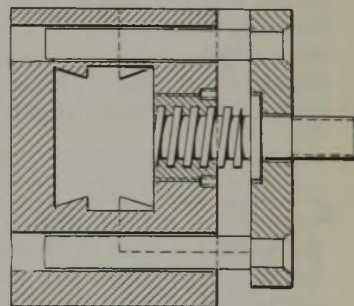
Anstellbarer Stauchkasten mit schwalbenschwanzförmiger Befestigung der Führungsbacken.
